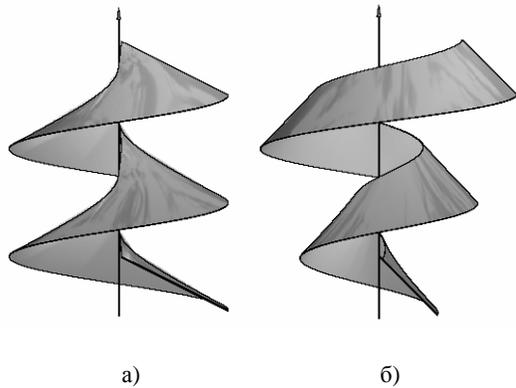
Образование цилиндрической (а) и конической (б) резьбовых поверхностей
